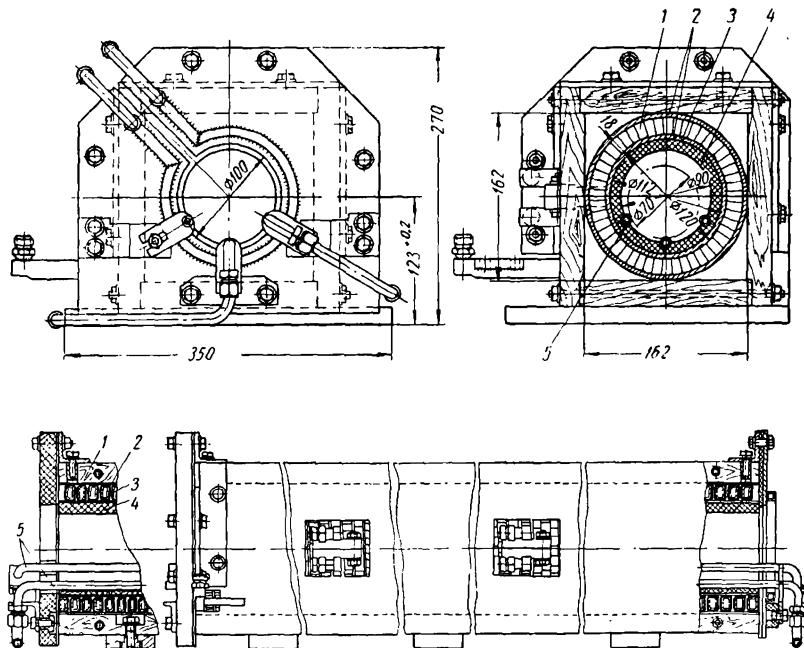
Индуктор для нагрева цилиндрических заготовок
